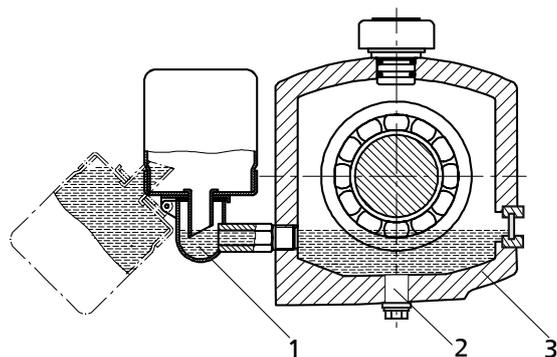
Масленка постоянного уровня с корпусом подшипника
